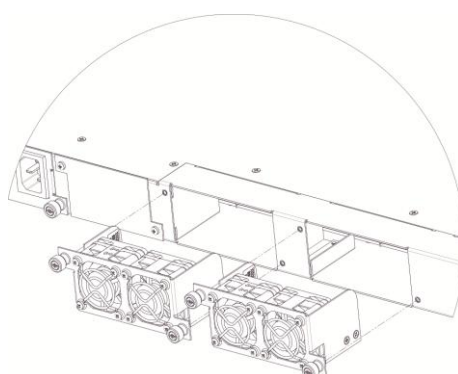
Блок вентиляции SMG-2016 rev. B. Крепление в корпус
